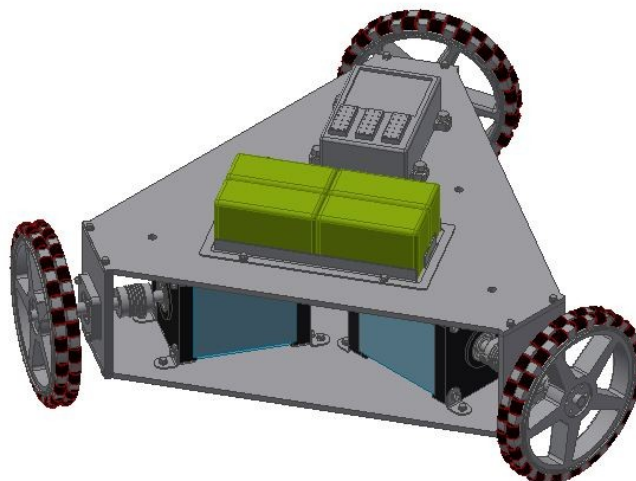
Pohonná jednotka: 1-elektromotor, 2-držák, 3-pružná hřídelová spojka, 4-příruba s ložiskem, 5-univerzální všesměrové kolo
